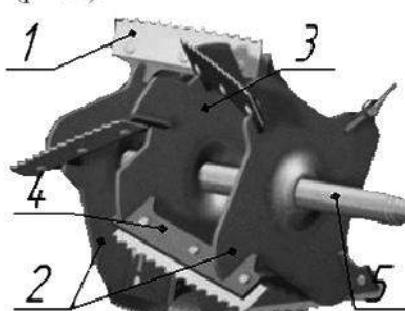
Загальний вигляд прискорювача різаної маси: 1 - лопатка; 2- диск боковий; 3- диск центральний; 4- траміч лопатки; 5- вал прискорювача
